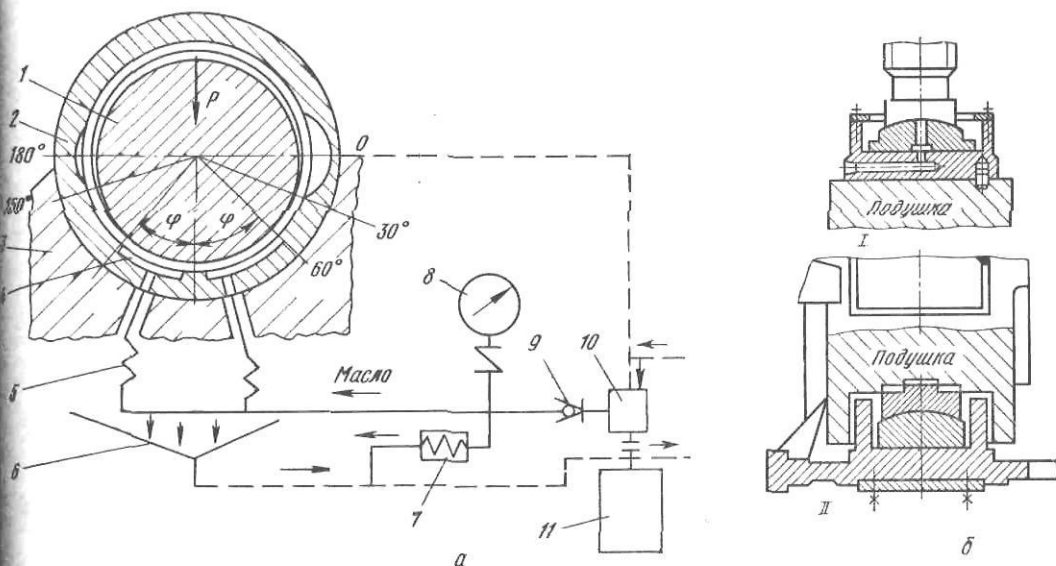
Схема гидростатодинамического ПЖТ с дополнительной системой гидростатического подпора а (1 — цапфа валка; 2 — втулка подшипника; 3 — корпус подшипника; 4 — дуговые узкие карманы; 5 — капиллярные трубки; 6 — сливные карманы; 7 — предохранительный клапан; 8 — манометр; 9 — обратный клапан; 10 — насос высокого давления; 11 — электродвигатель; б — подпятники для самоустановки верхней (I) и нижней (II) подушек
